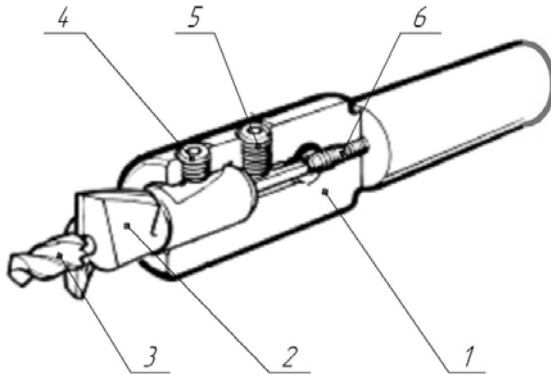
Свердло-цеківка фірми Granlund Tools AB
